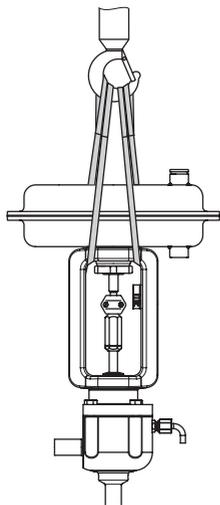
Тип 3349 с Тип 3271 без подъемного рыма
